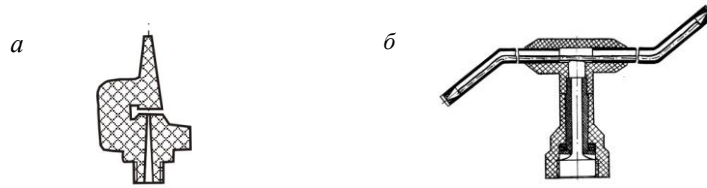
Дождевальные насадки конструкции КазНИИВХ: а – форсунка дождевальная; б – насадка карусельная
